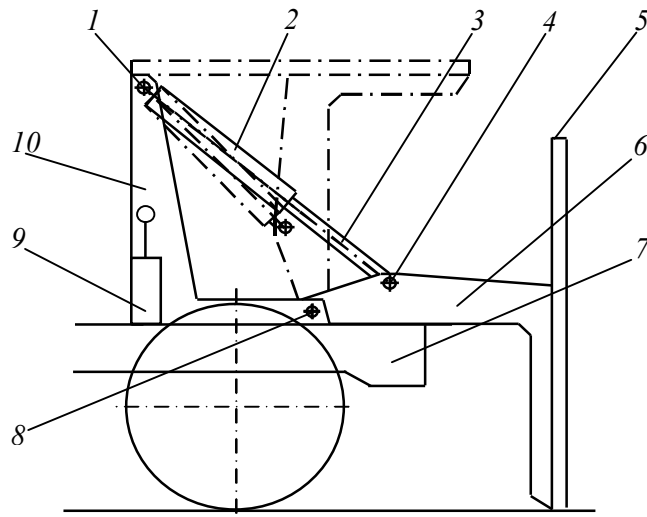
Пристрій повертання силового бар'єра з транспортного положення в робоче
